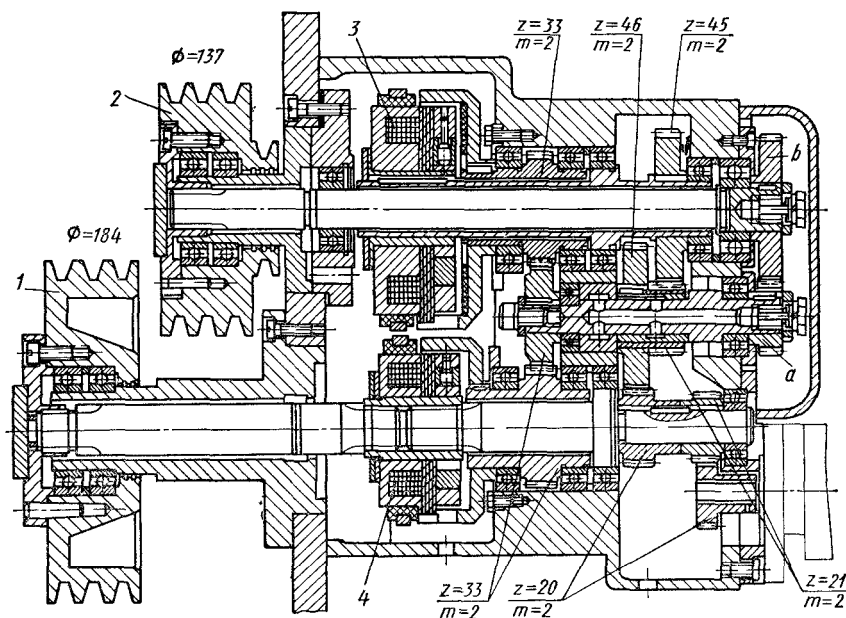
Коробка скоростей револьверного станка мод. 1Н318
